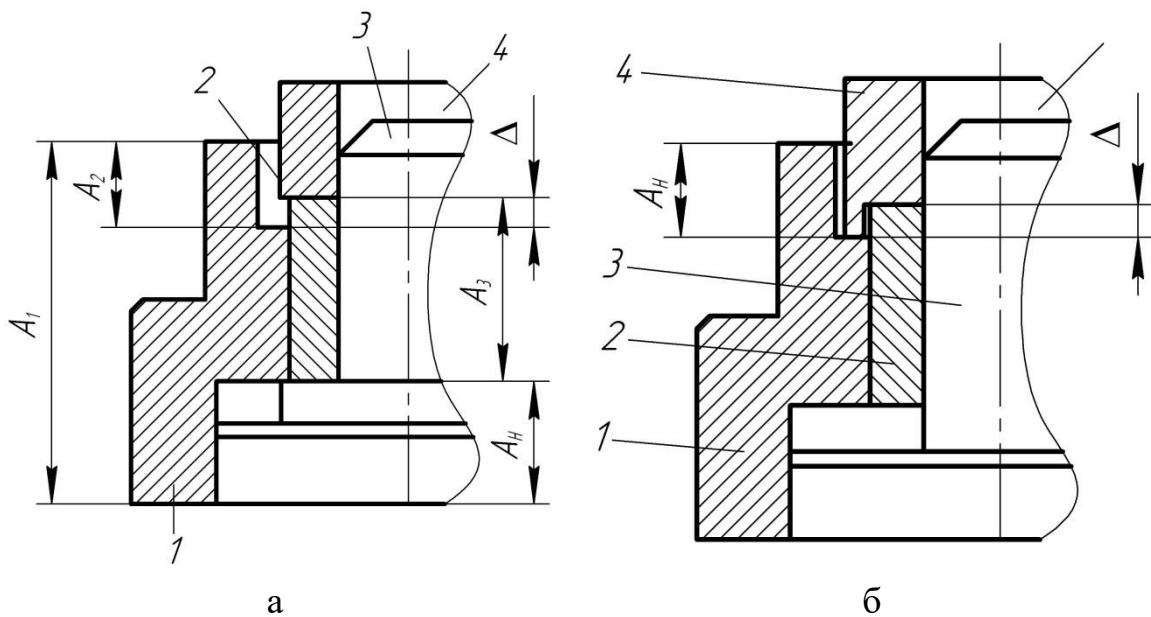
Варианты схем базирования в приспособлениях для сборки втулки с корпусом при необходимости выдерживания размера A
